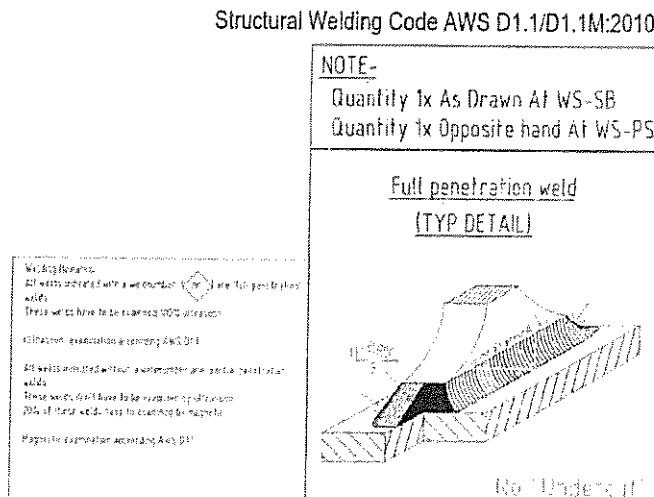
Requerimientos de soldadura (Ref. L18035-KAL-PLN-24C0 1)
